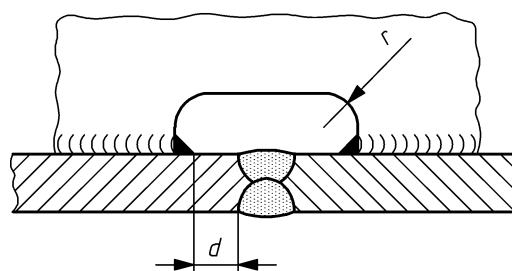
Raidisseurs soudés perpendiculairement à une soudure longitudinale
